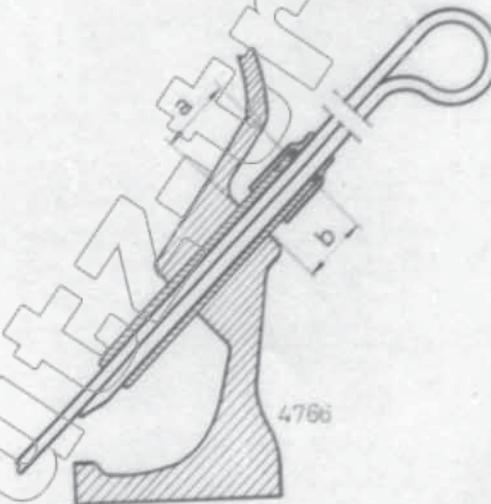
Einbau des Führungsrohres zum Ölmeßstab F 2L 712
